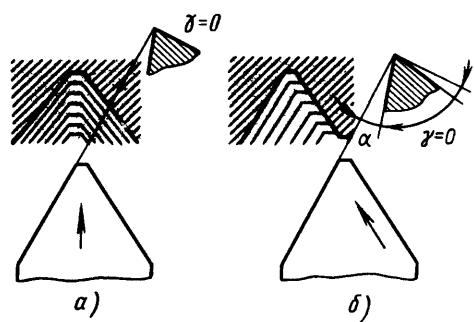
Схемы (а, б) установки резца при нарезании резьбы
